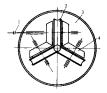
三辊式机架内齿轮传动机架结构示意 1-输入轴; 2--轧辊; 3--机架; 4--锥齿轮
